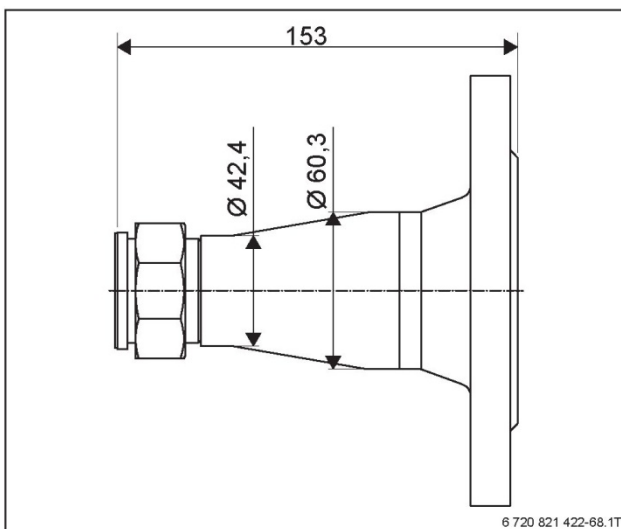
Переходная деталь DN 50/PN 16 - G 1 1/2" (размеры в мм)
